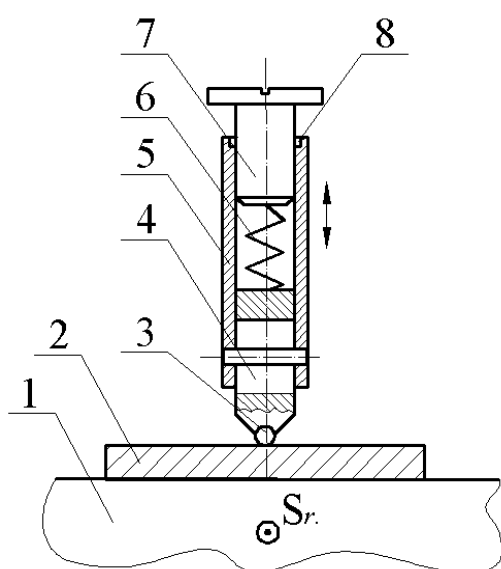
Кінематична схема пристрою для вібраційного обкочування плоских поверхонь
